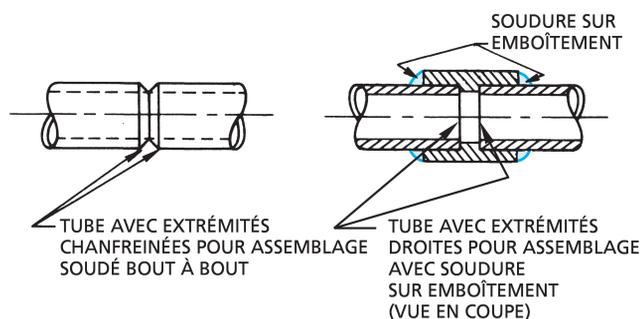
■ Préparation des extrémités de tubes pour assemblage soudé bout à bout et assemblage soudé sur emboîtement.
